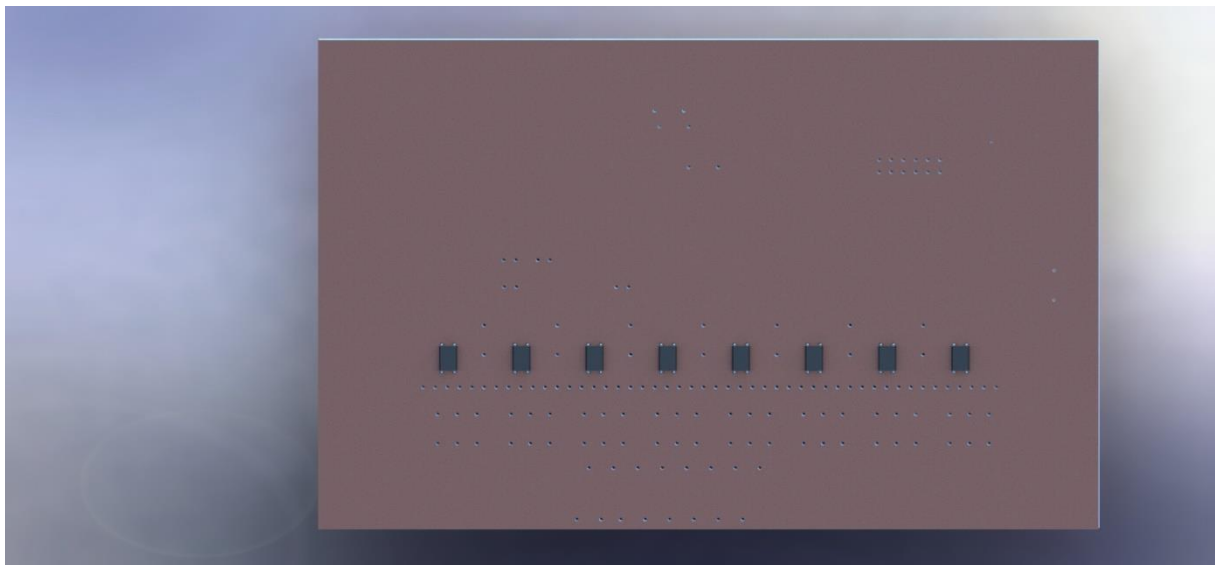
PCB entradas: Posición elementos aislantes (Optoacopladores).
